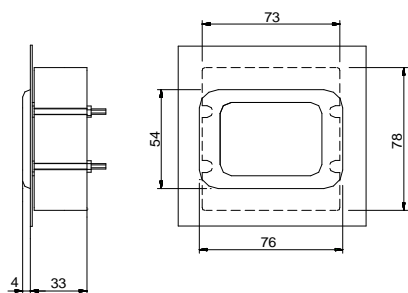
Afficheur pour fixation au moyen de goujons soudés sur la boîte à boutons
